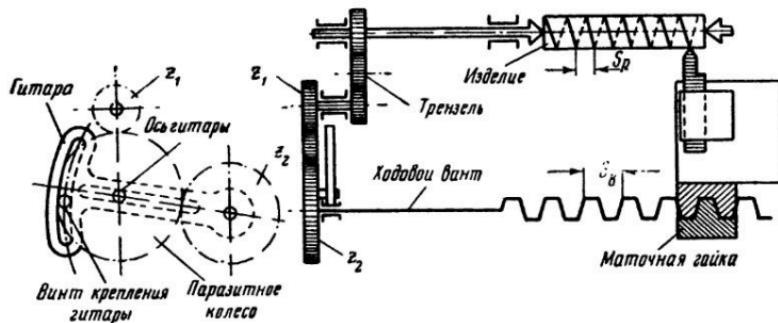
Кинематическая схема механизма подачи суппорта токарного станка (взаимосвязь между вращением обрабатываемой детали и движением резца).
